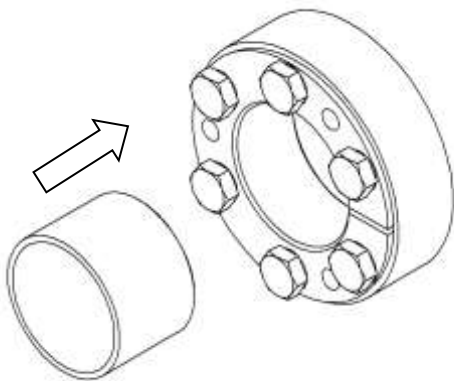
Aufschieben des Außenspannsatzes auf Hohlwelle
